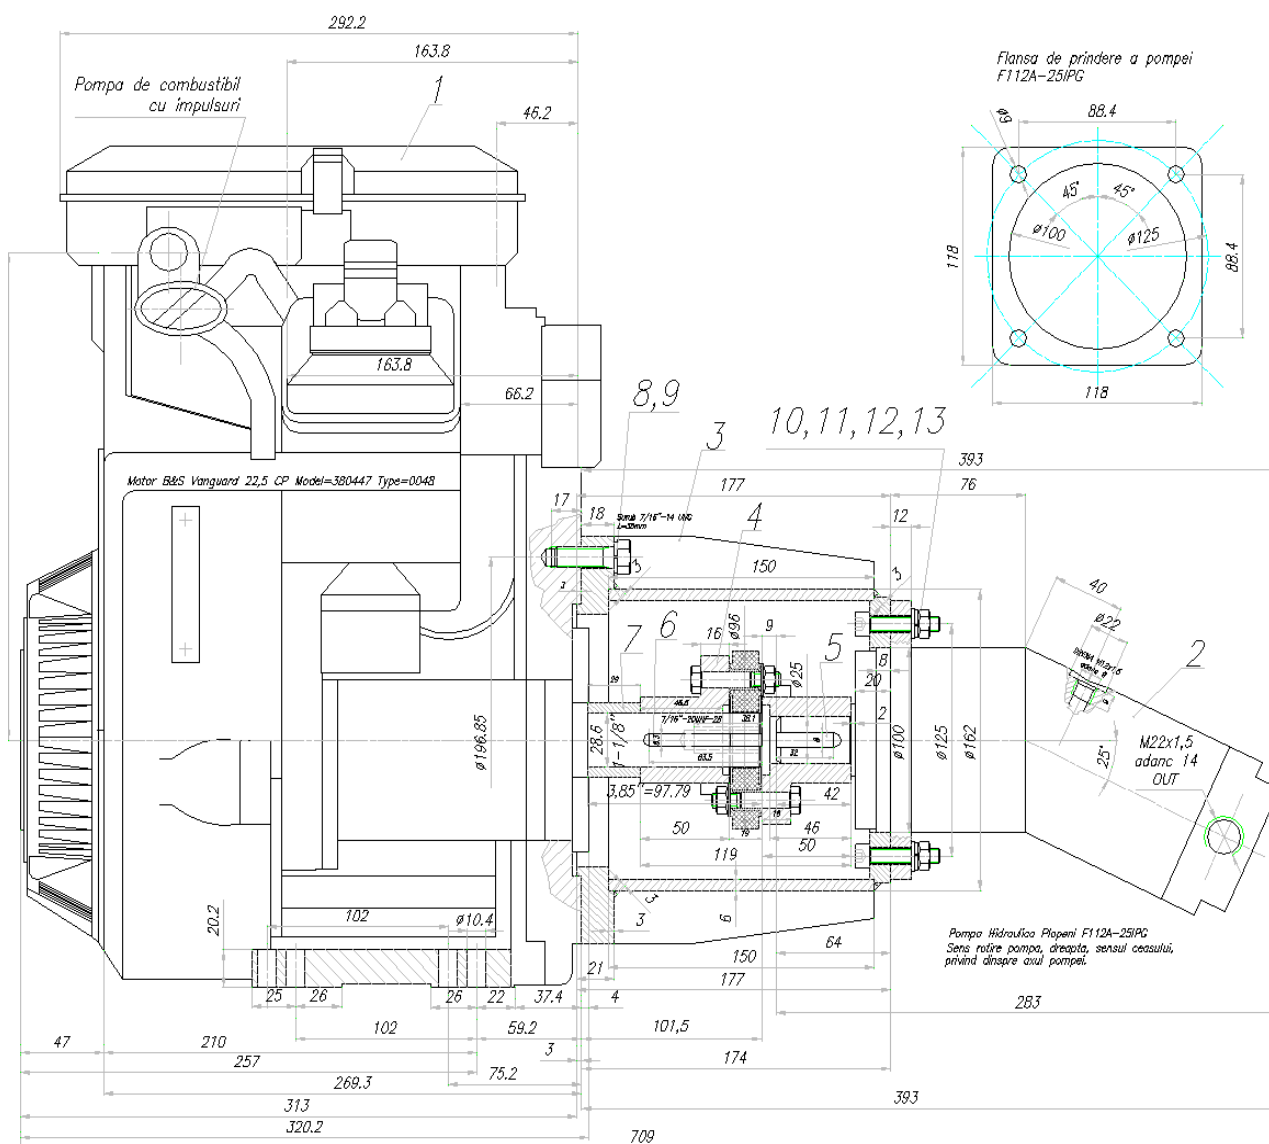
Desenul "Grup motor-pompa hidraulică FG40"
